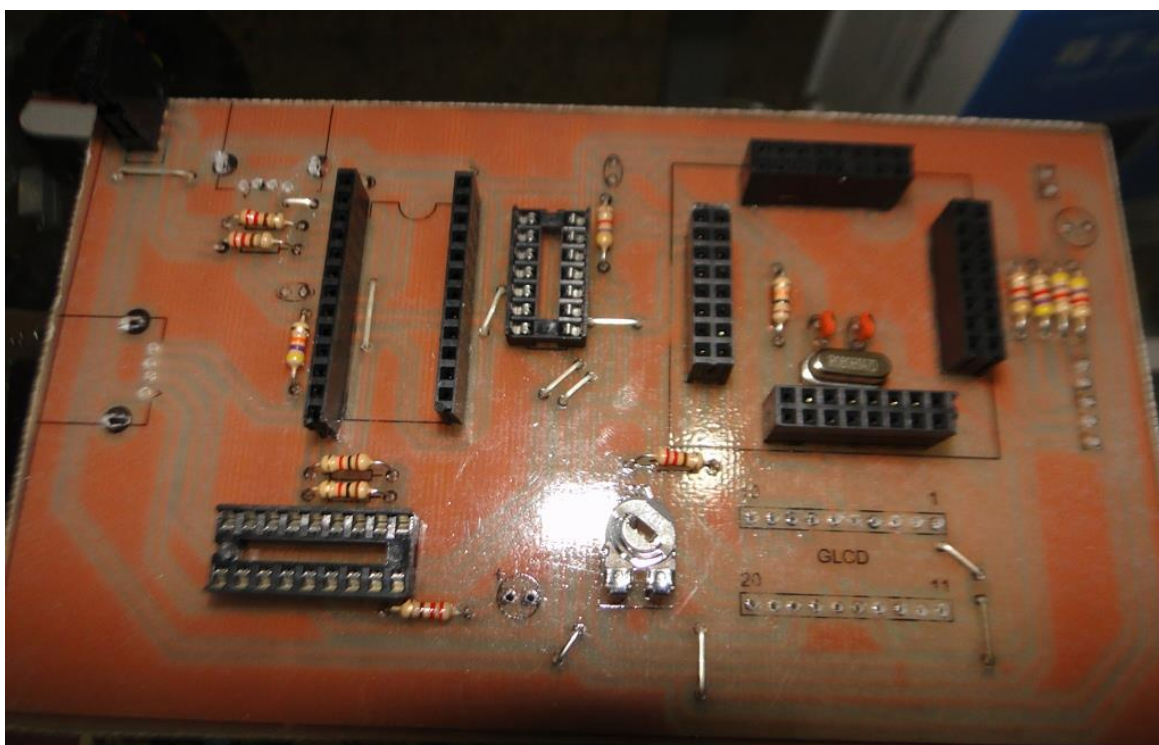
Proceso de soldado de los elementos en la placa
